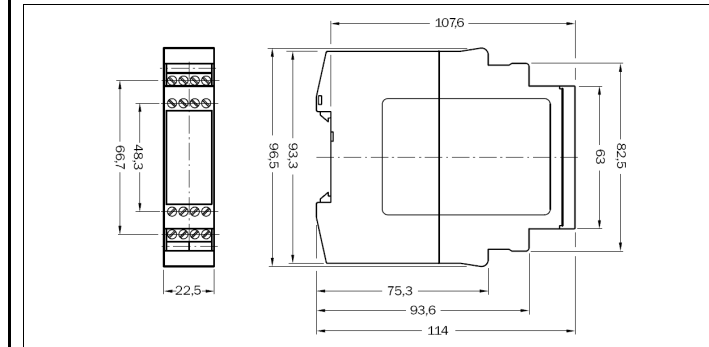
Maßbild UE11-4DX mit Schraubklemmen (mm)
